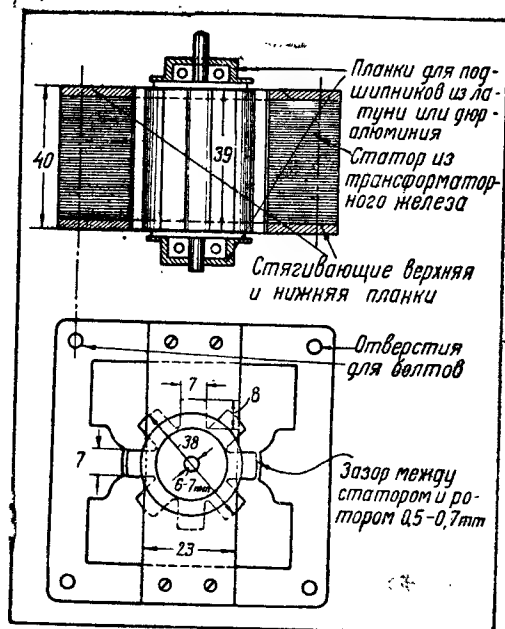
Ротор и статор мотора — вид сбоку и сверху
